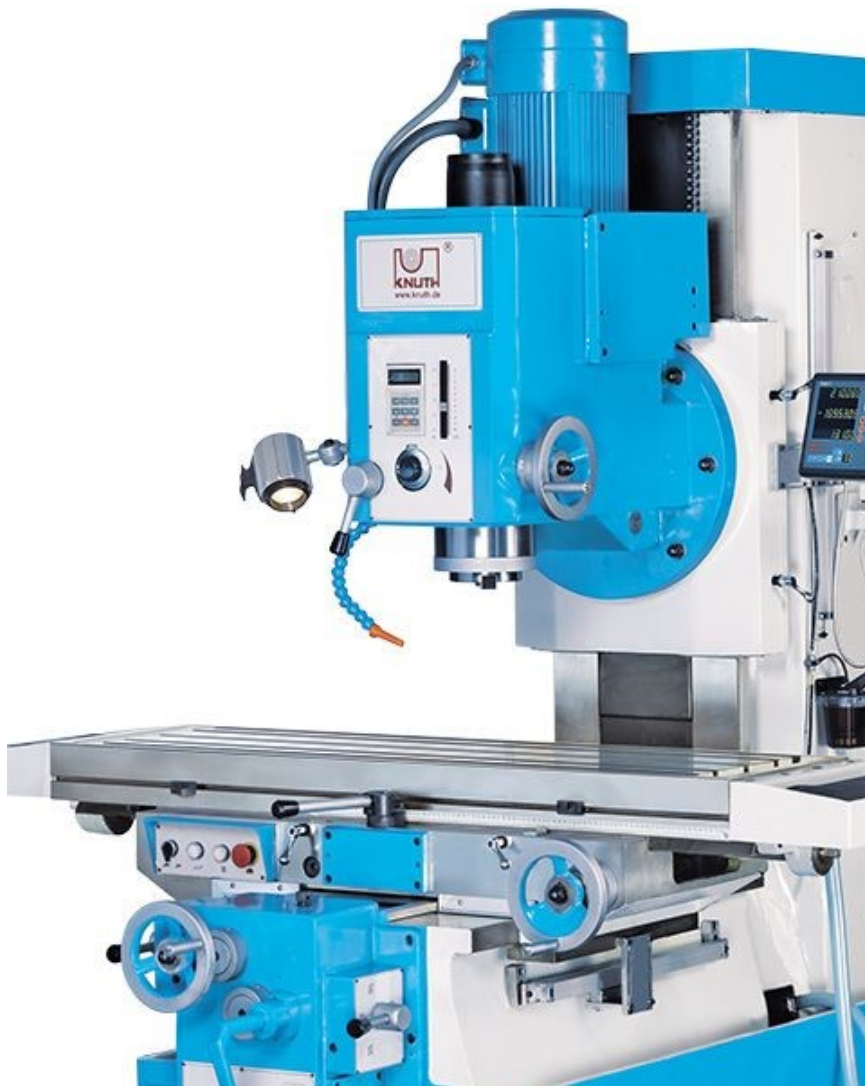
20. Повздовжній фрезерний верстат KV 1400 для інтенсивної обробки великогабаритних деталей
